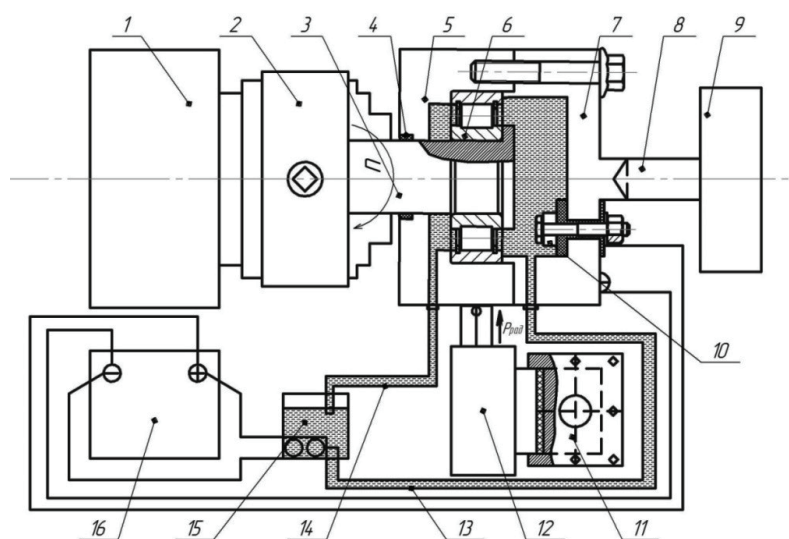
Схема устройства для электрохимикомеханической обработки подшипника качения:
